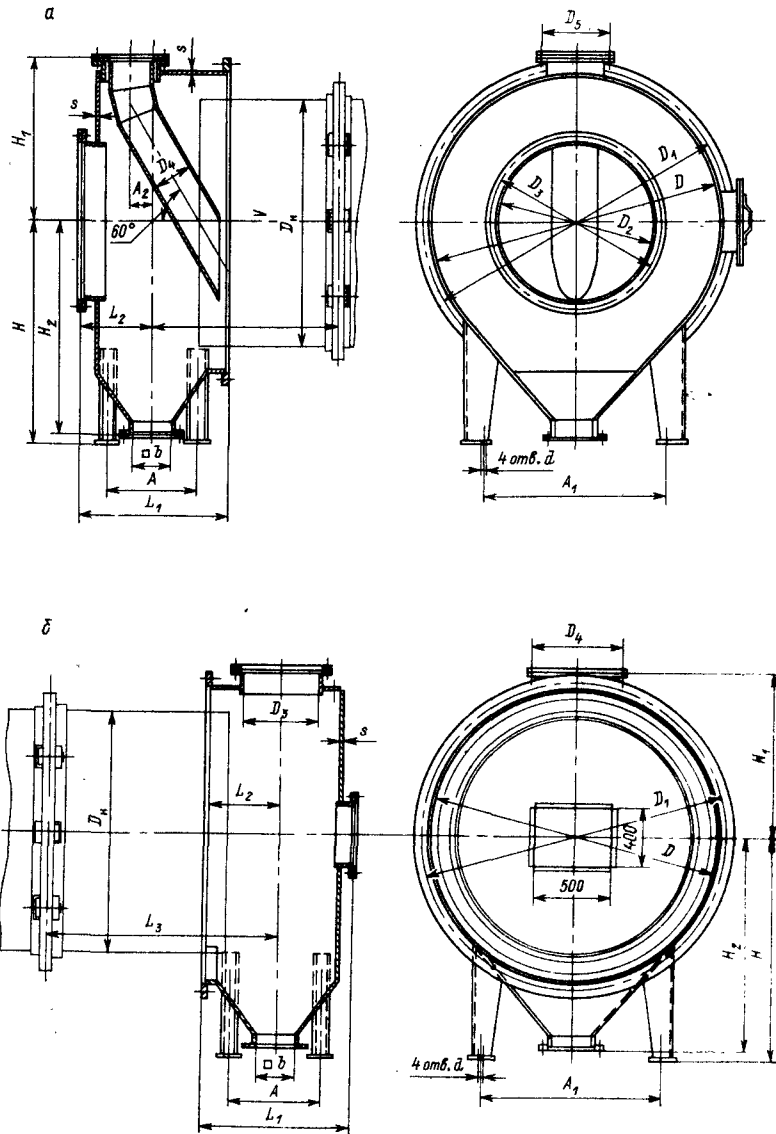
Загрузочная (а) и разгрузочная (б) камеры для сушилок с прямоточным движением потоков
